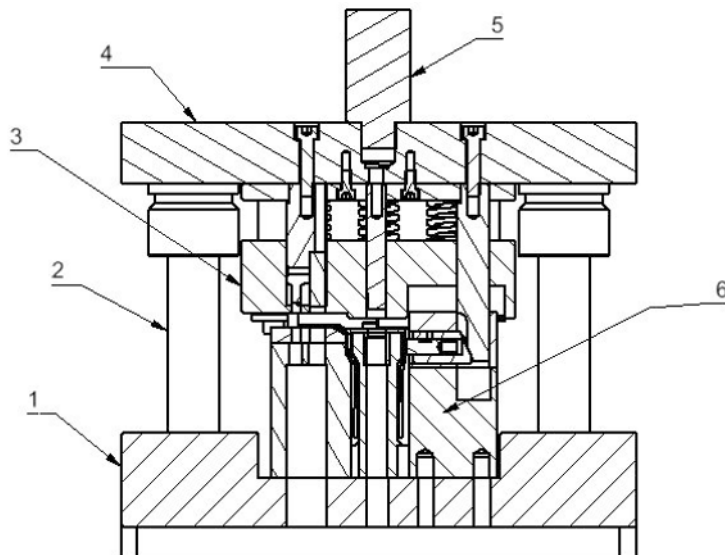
Vier-Säulen-Stanzwerkzeug
